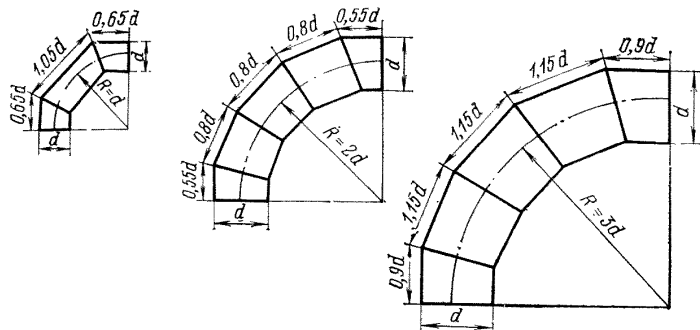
Сварные колена из нескольких звеньев.
